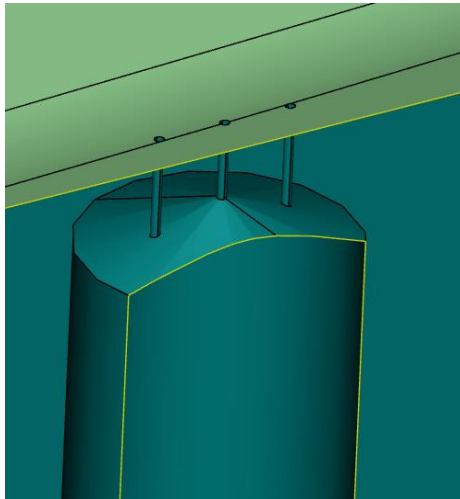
Schnitt durch 3 der über 800 Vakuumborungen im Werkzeug
